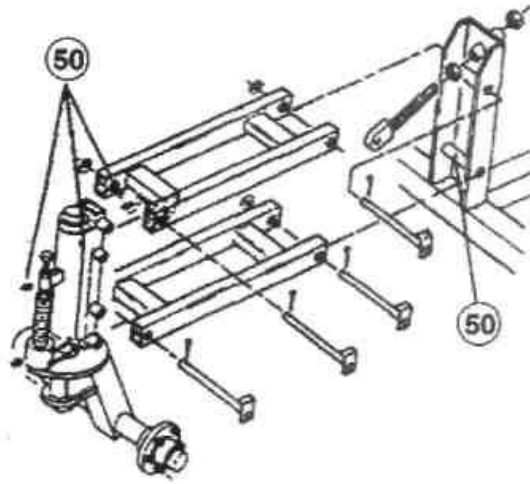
Точки мащення поворотного вала і передньої підвіски.
